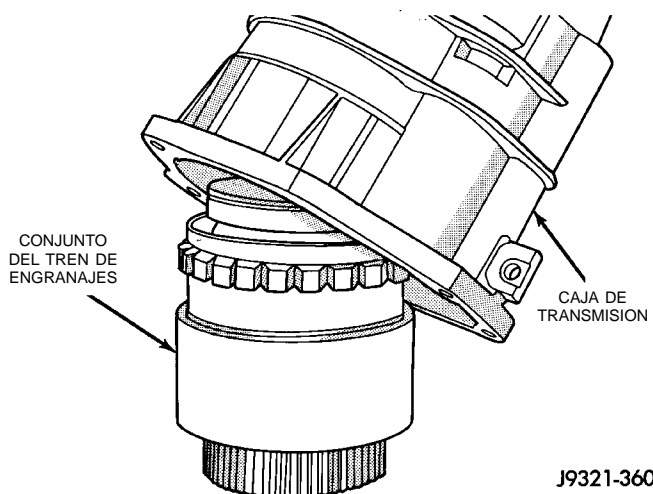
Desmontaje de la caja de transmisión del conjunto del tren de engranajes
